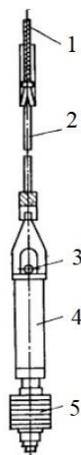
Устройство сваба: 1 – канат, 2 – подвеска, 3 – клапан, 4 – патрубок, 5 – поршень
